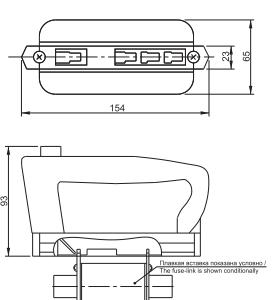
Габаритные размеры рукоятки для смены плавкой вставки / Figure 4 – Overall dimensions of a handle for fuse-link replacement
